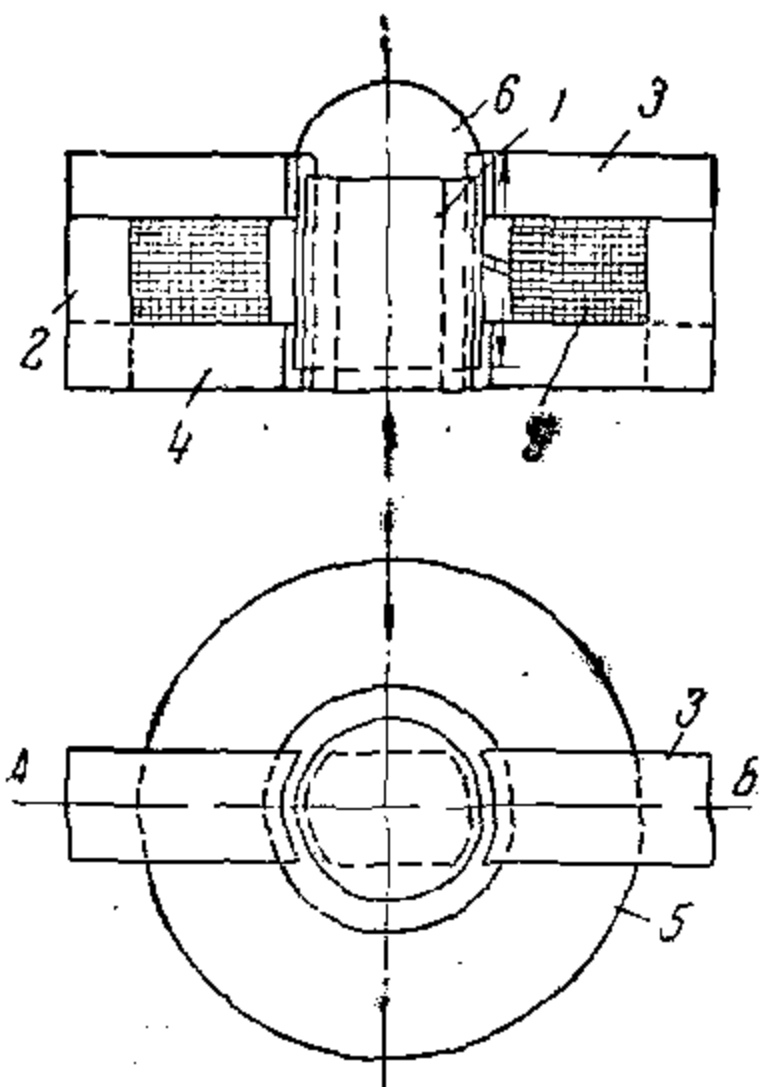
Схема индукционного прибора для отжига алюминиевых цилиндров:
